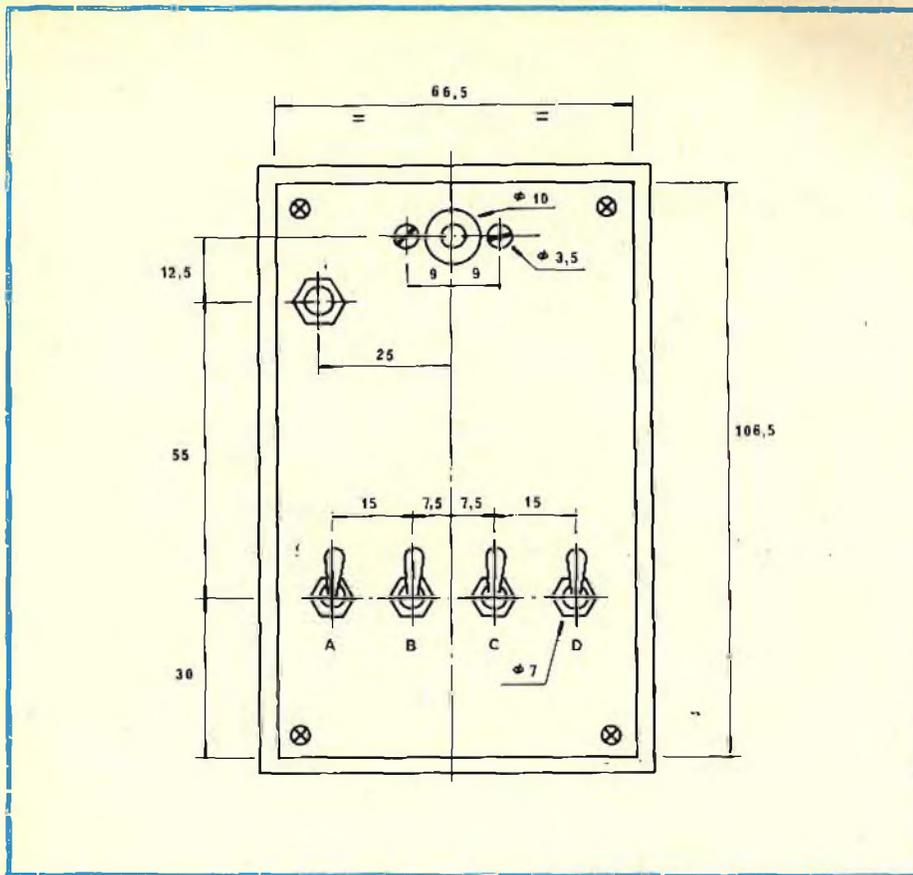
Vista d'insieme del frontale per l'assemblaggio in contenitore Teko.
